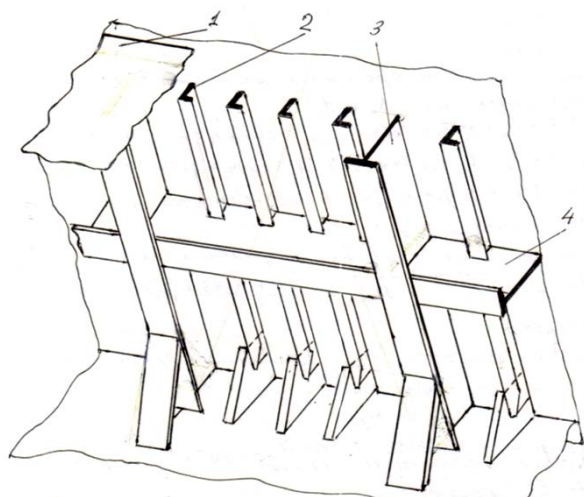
Бортовое перекрытие с холостыми и рамными шпангоутами:
